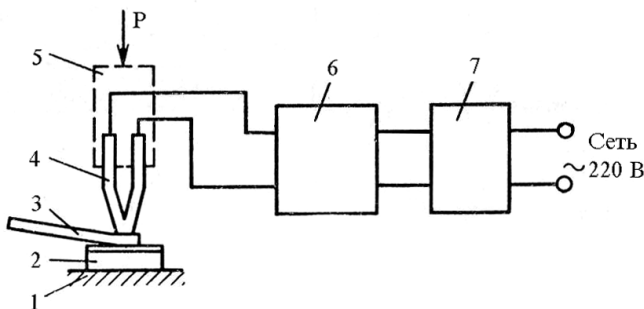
Схема сварки давлением с косвенным импульсным нагревом V-образным инструментом: 1 – рабочий стол; 2 – подложка; 3 – проводник; 4 – инструмент; 5 – сварочная головка для создания давлением; 6 – источник питания; 7 – реле времени
